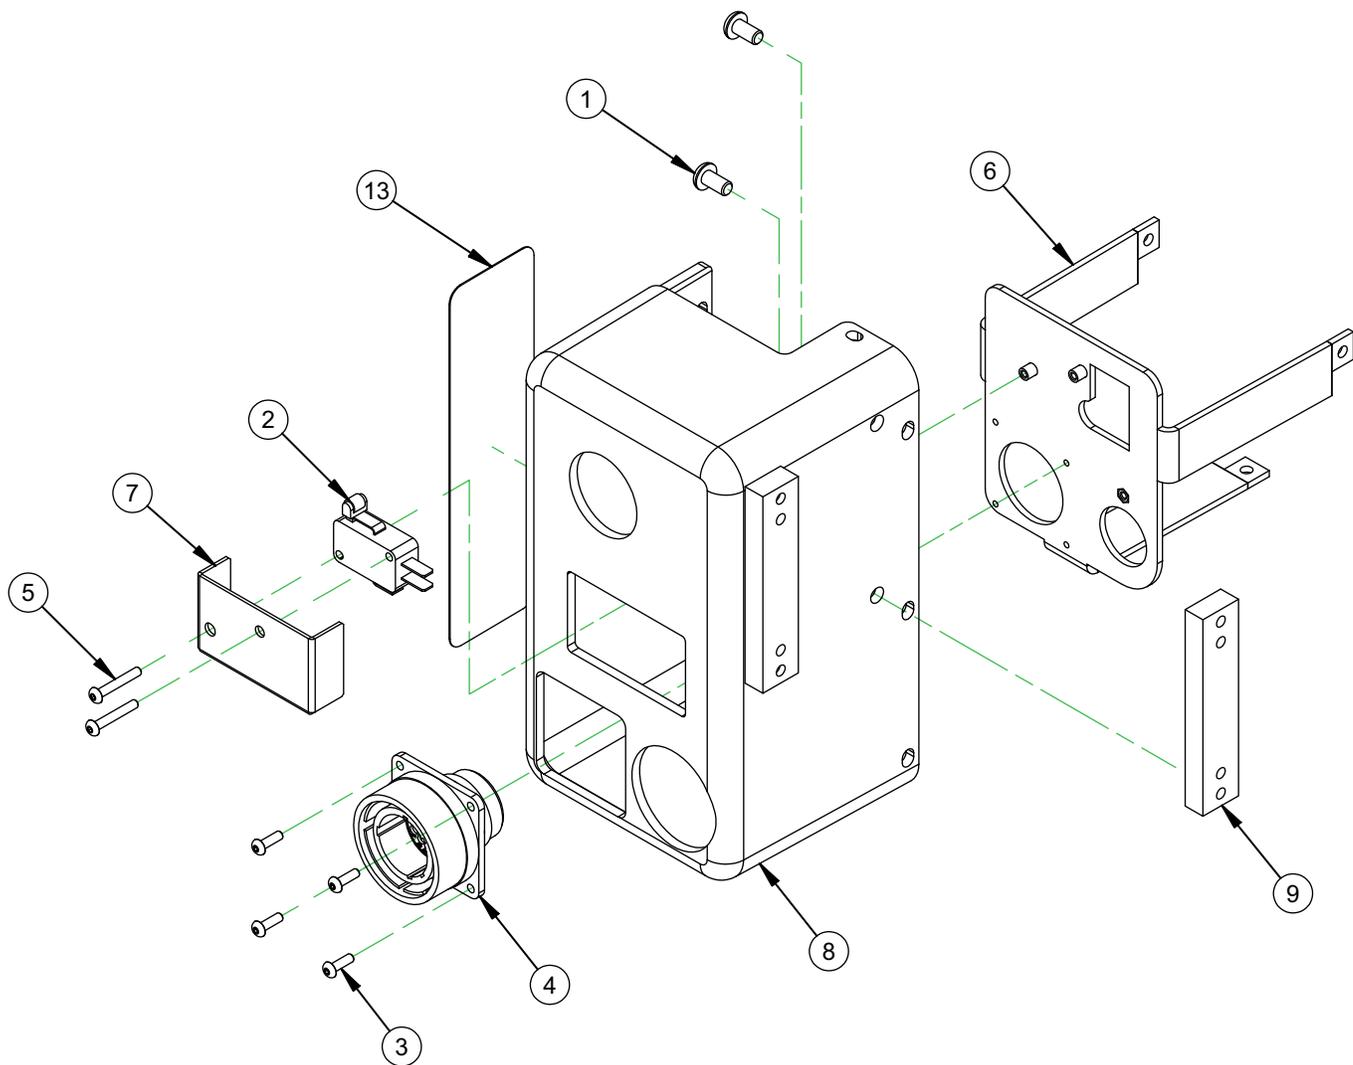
LISTE 2 DES PIÈCES DE L'ENSEMBLE DE TÊTE DE SOUDAGE (RÉF. 91808)
